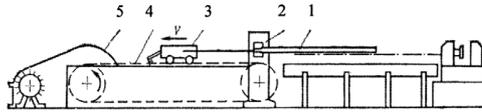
Схема цепного волочильного стана Подготовка заготовки
